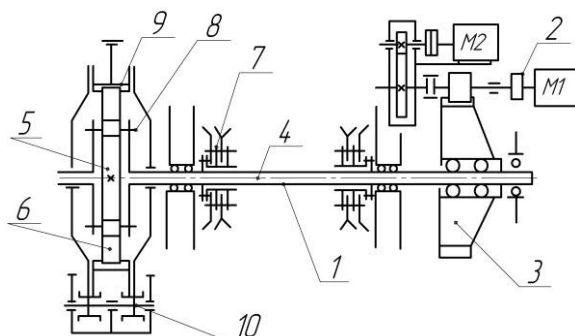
Схема однодвигунового привода ківшевого ланцюга з планетарною муфтою-гальмом:
